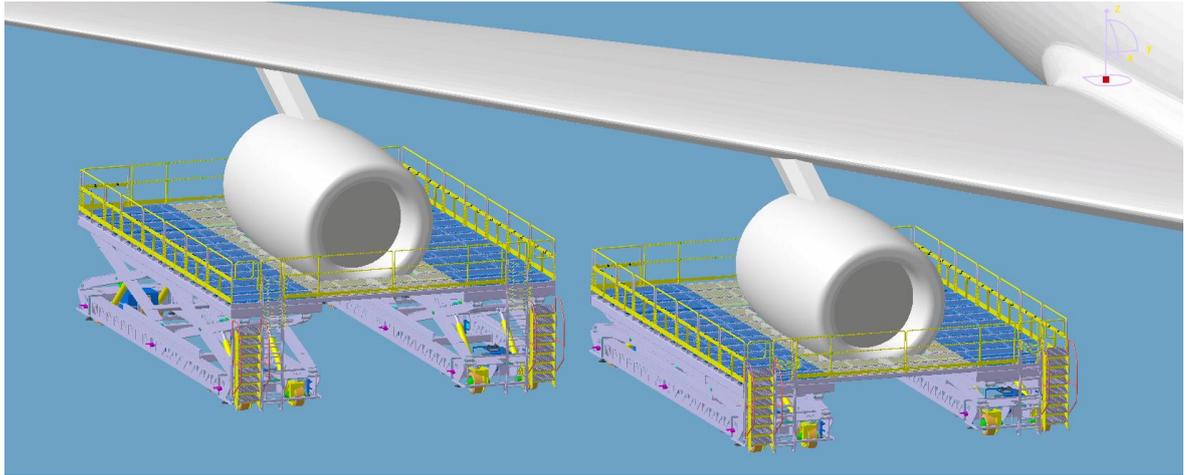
Detalle de la posición en la zona de motores del nuevo diseño de plataforma flexible
